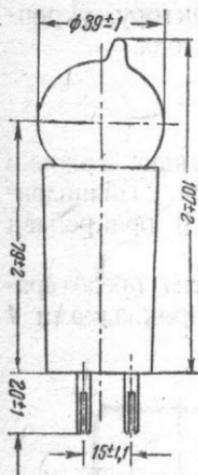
Общий вид и габаритные размеры фотоэлемента
